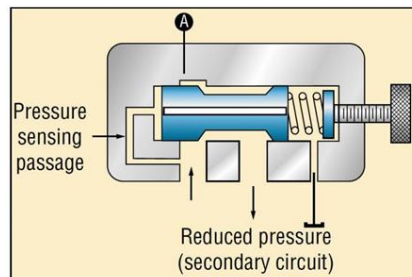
Válvula reductora de presión (*Engineering Essentials: Pressure-Control Valves, 2012*)
